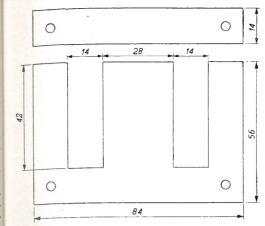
Dimensioni, in mm. del ferro del trasformatore T3. Lo spessore del lamierino è di 0,5 mm.
